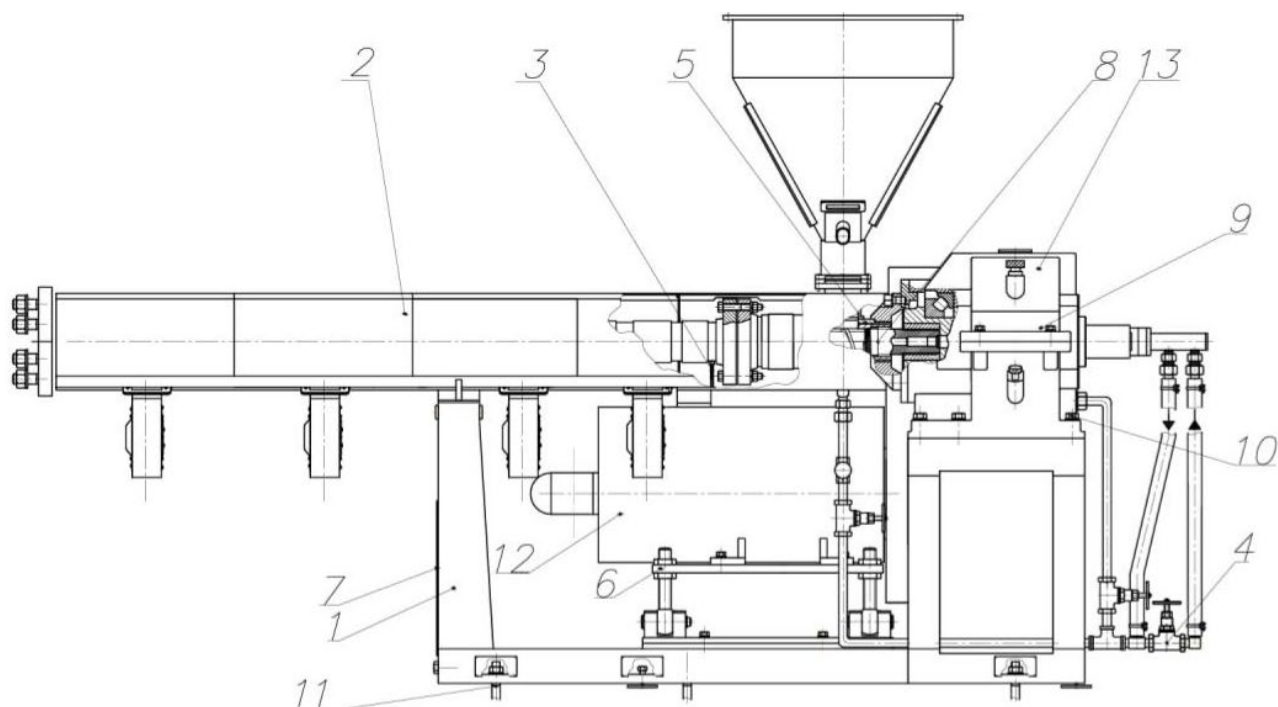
Конструкція одночерв'ячного екструдера: 1 – рама; 2 – кожух корпуса; 3 – бункер; 4 – система охолодження; 5 – корпус; 6 – воронка завантажувальна; 7 – черв'як; 8 – втулка; 9 – плита несуча; 10 – редуктор; 11 – вентилятор; 12 – нагрівач; 13 – розвід проводів
